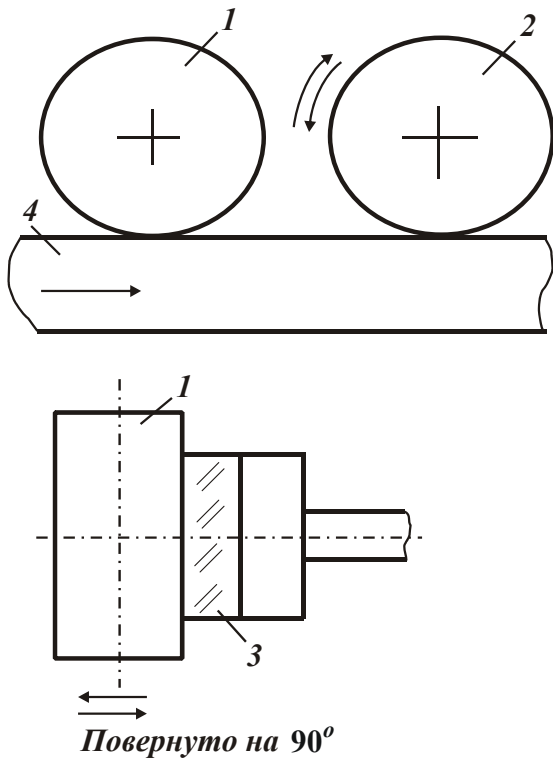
Схема обкатки в процессе абразивно-шлифовальной обработки: 1 – обкаточный круг; 2 – шлифовальный круг; 3 – вибратор, приводящий в движение обкаточный круг; 4 – обрабатываемая деталь.
